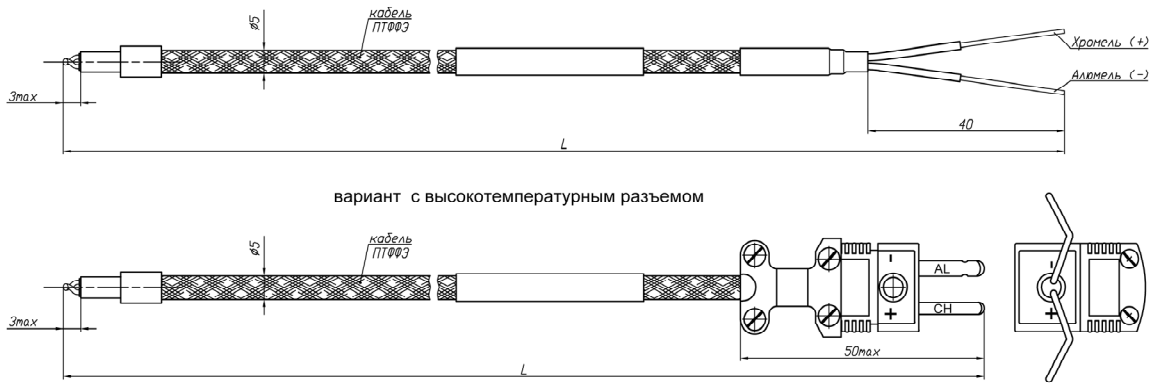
б - Габаритный чертеж термопары РГАЖ5.182.002-13
